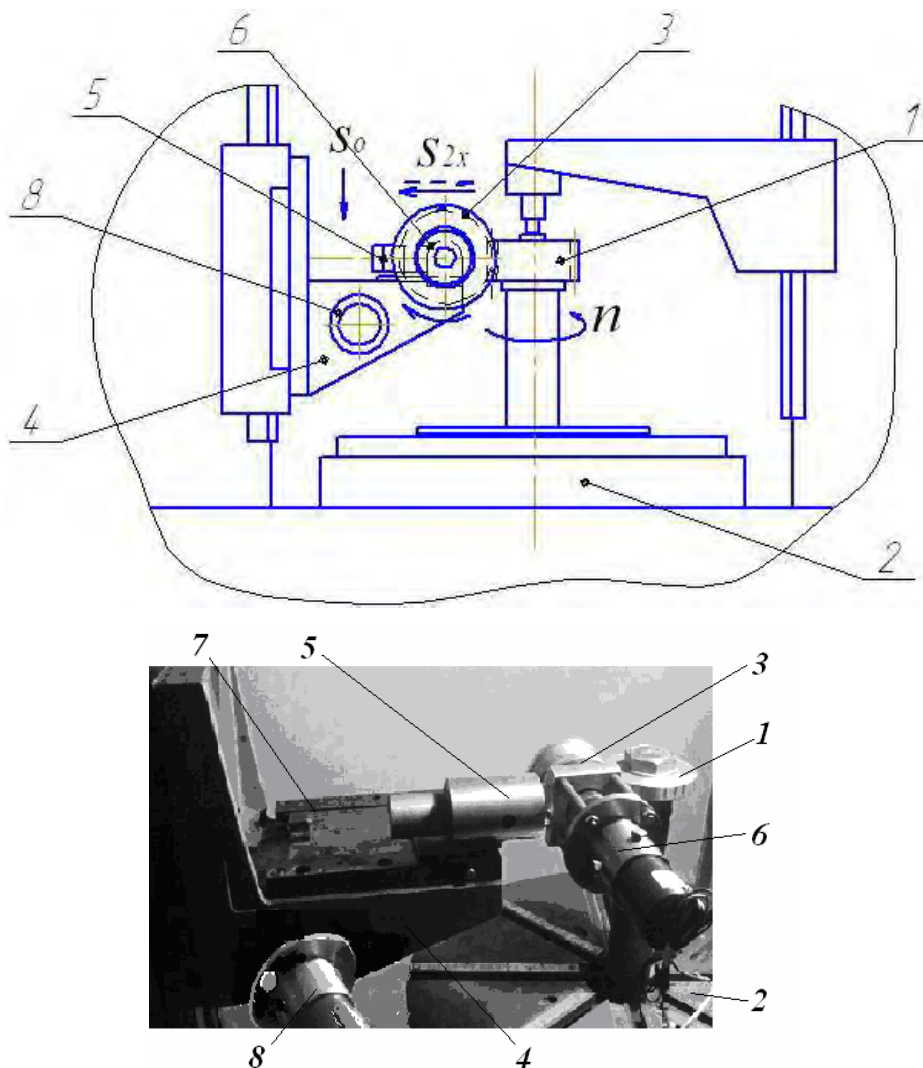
Робочий простір зуборезного верстата з керованими приводами для нарізання коліс за РК-способом
